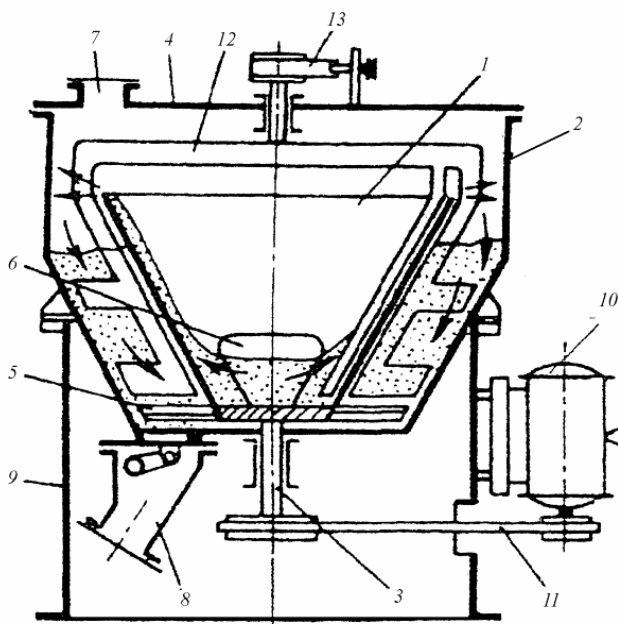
Центробежный волчковый смеситель типа ЦВ
